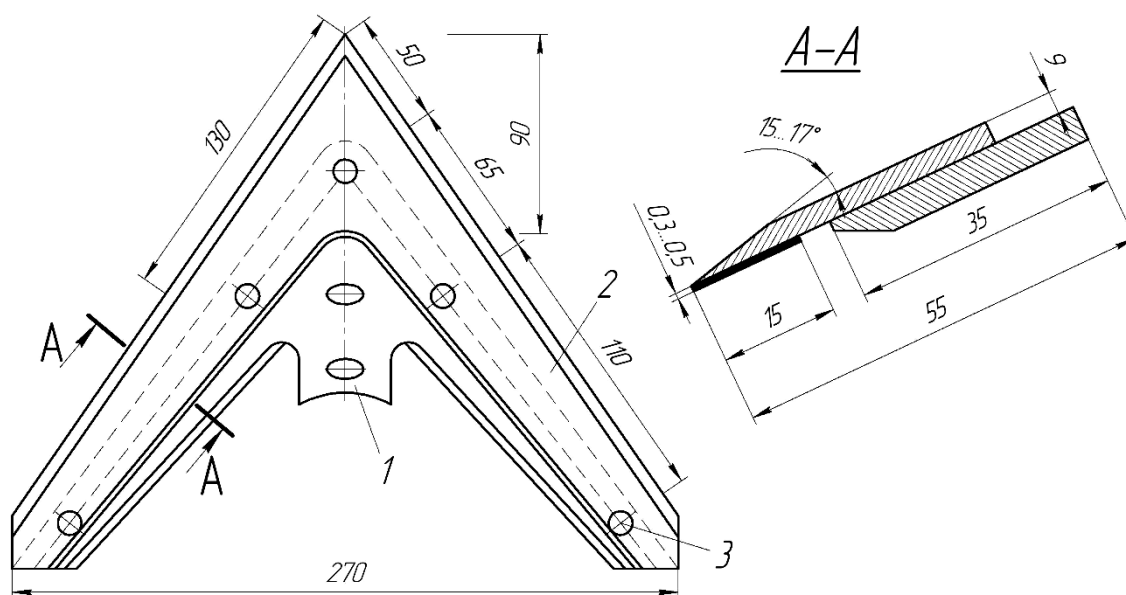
Конструкція складової культиваторної лапи по І.Д. Канівцю [2]: 1 - корпус; 2 - змінне лезо; 3 - заклепки.
